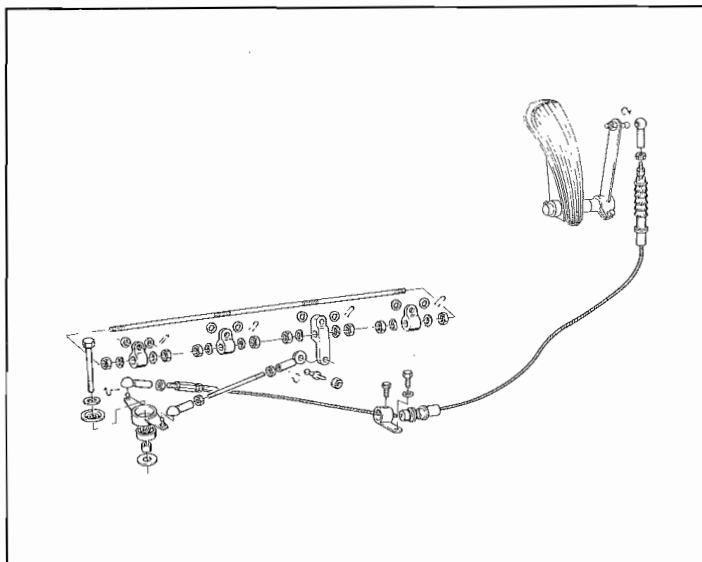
Leveraggio comando carburatori cambio meccanico
